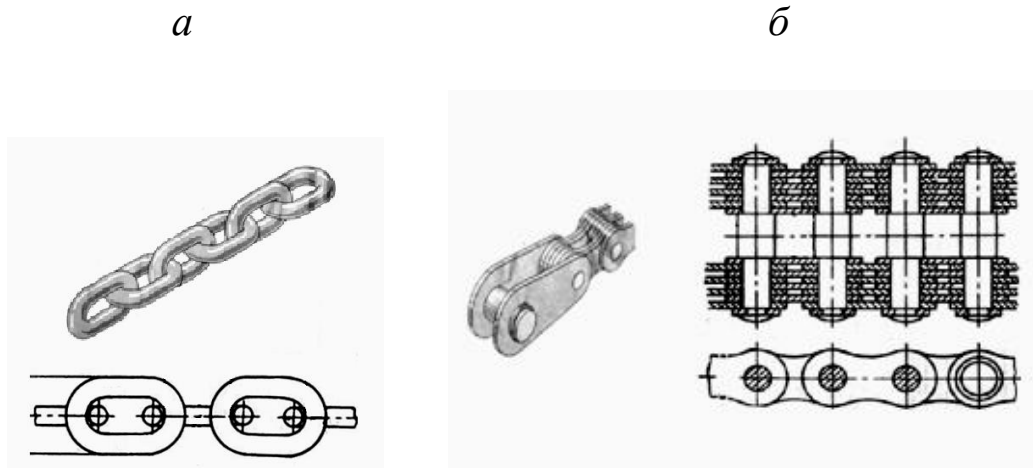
Вантажні ланцюги: зварний (а), пластинчастий (б)
